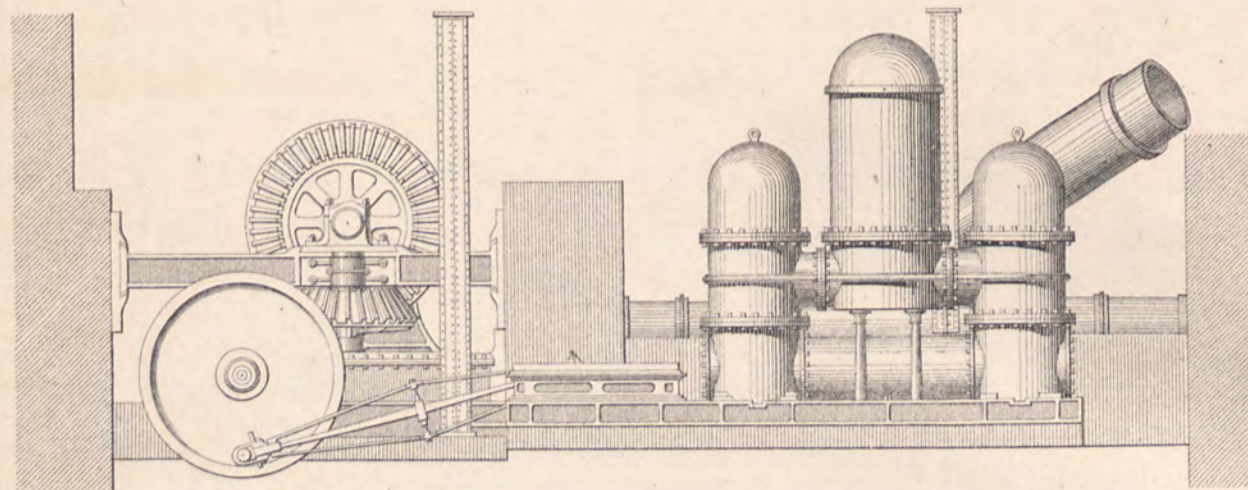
Coupe longitudinale par l'axe de la turbine.
